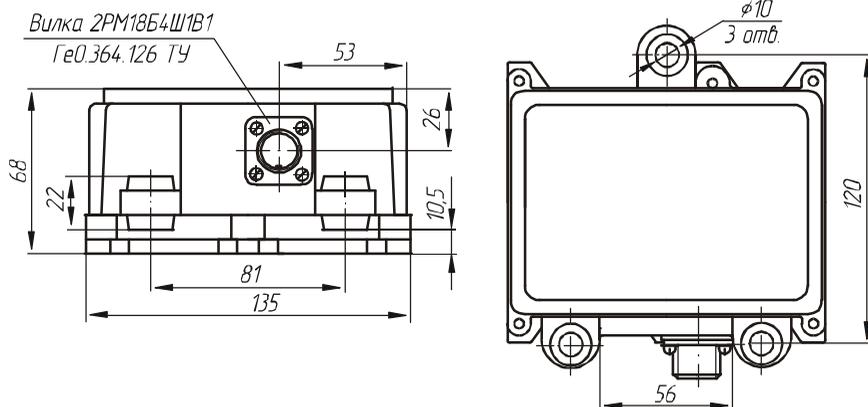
Габаритные и присоединительные размеры датчика приближения к ЛЭП
